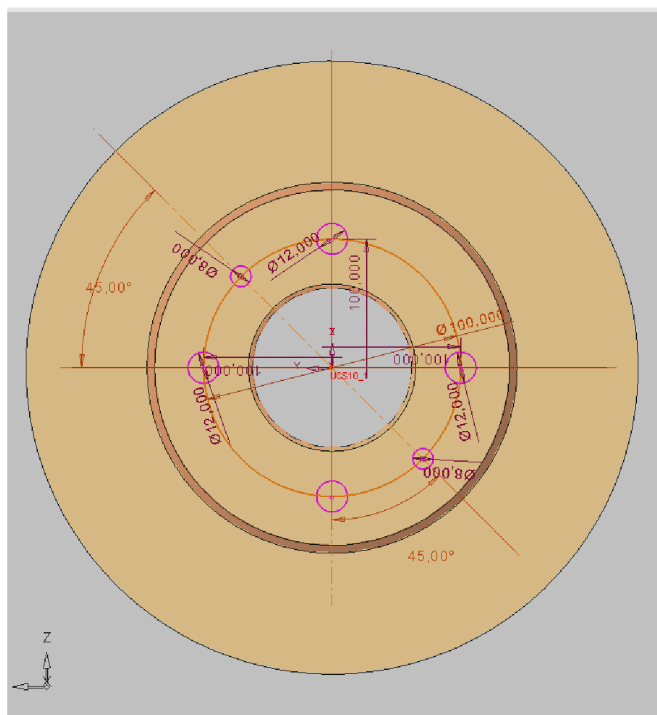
Ескіз деталі відповідно розмірам
